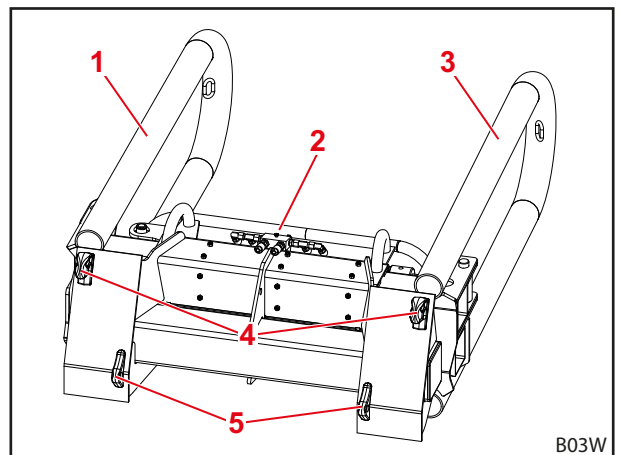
Oppbygging ballegriper Pro H – sett bakfra
